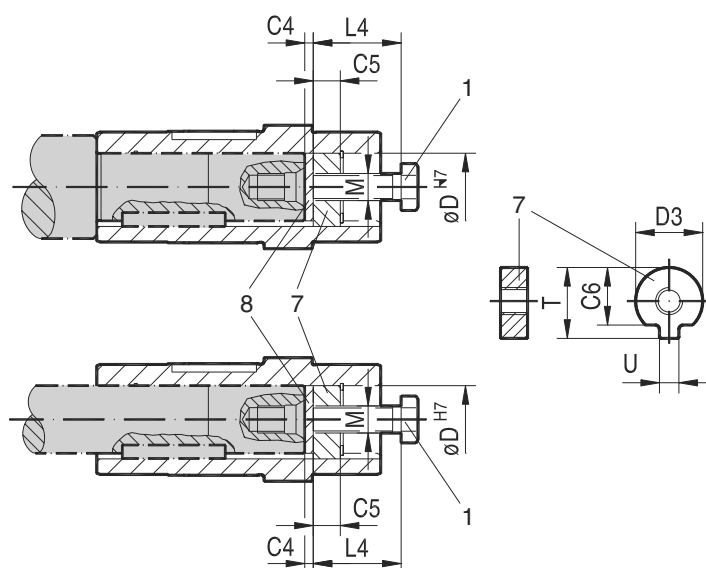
Kit de montagem/desmontagem SEW-EURODRIVE
